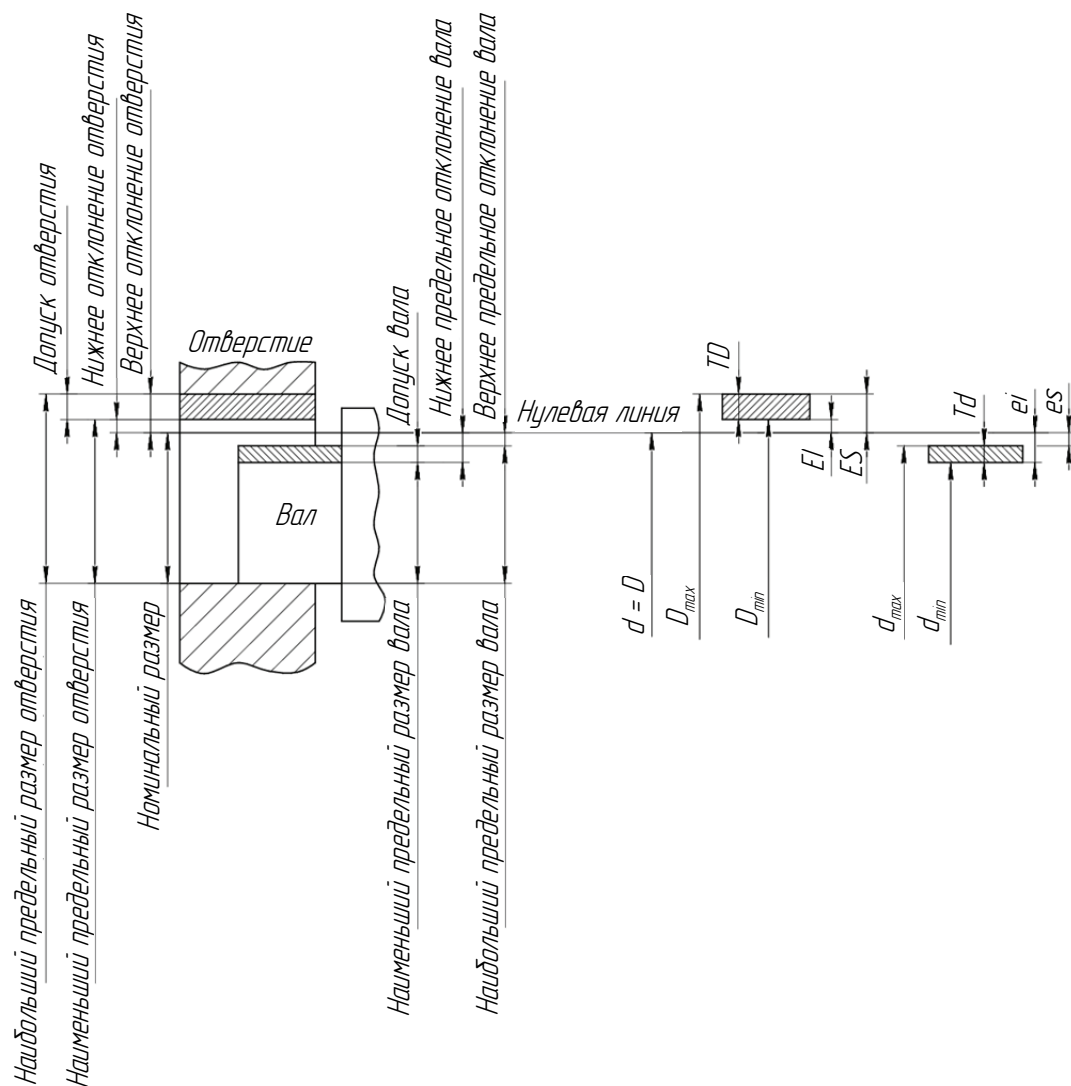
Основные размерные параметры и схема расположения полей допусков
